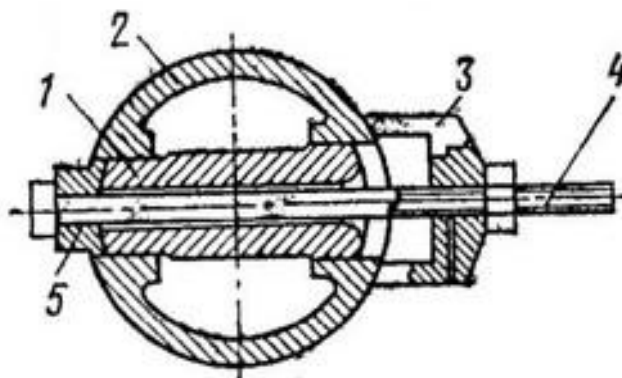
Приспособление для выпрессовки поршневых пальцев
